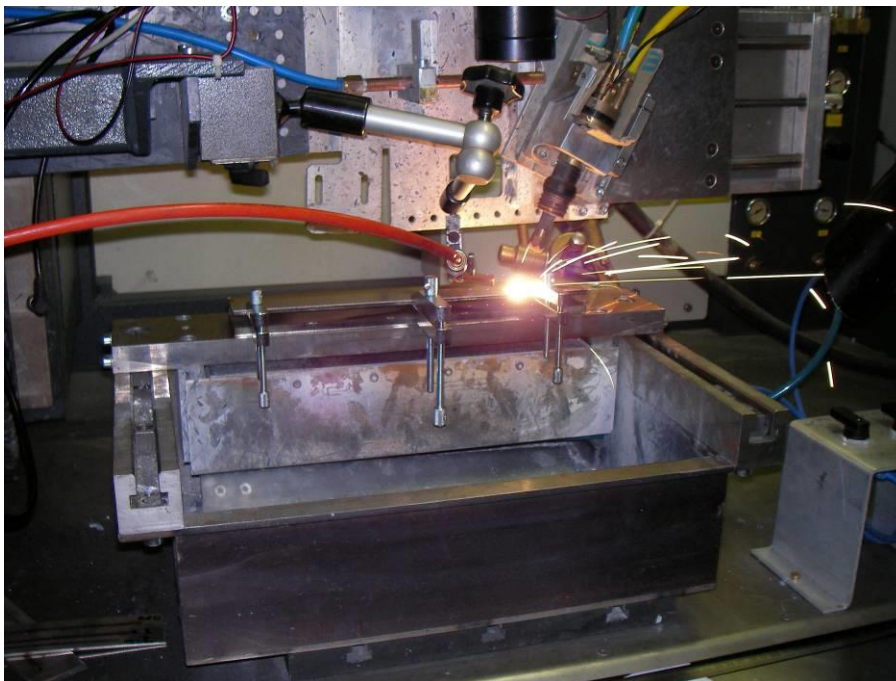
Schweißung mit Parallelzwingen zur Spaltreduzierung am Bauteil
